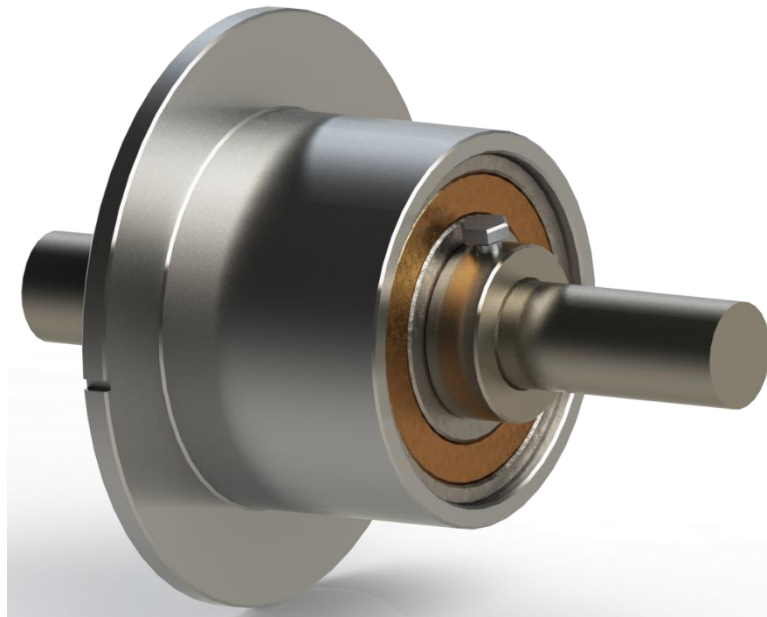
Hasil *rendering* unit penggerak *pulper mobile*.
